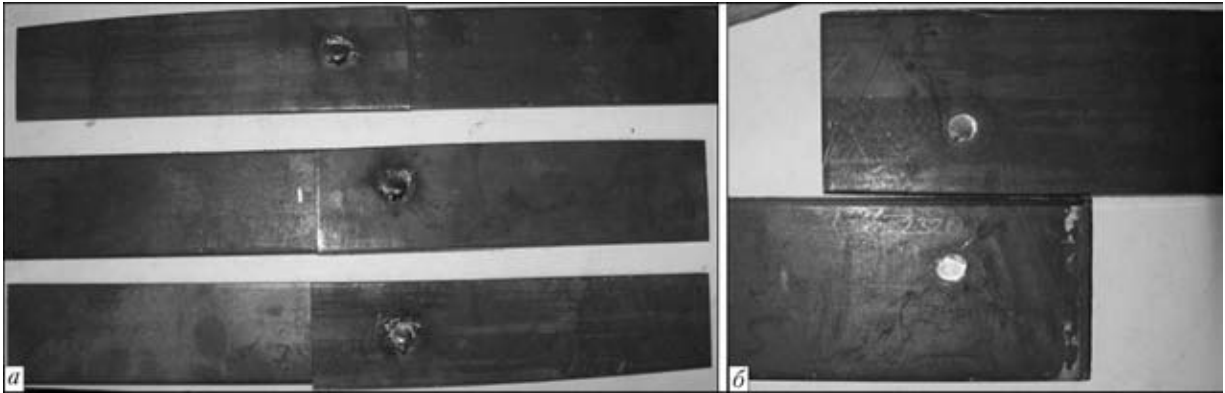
Вид образцов точечных сварных соединений до испытаний на растяжение (а) и после разрушения сварных точек по механизму среза (б)
